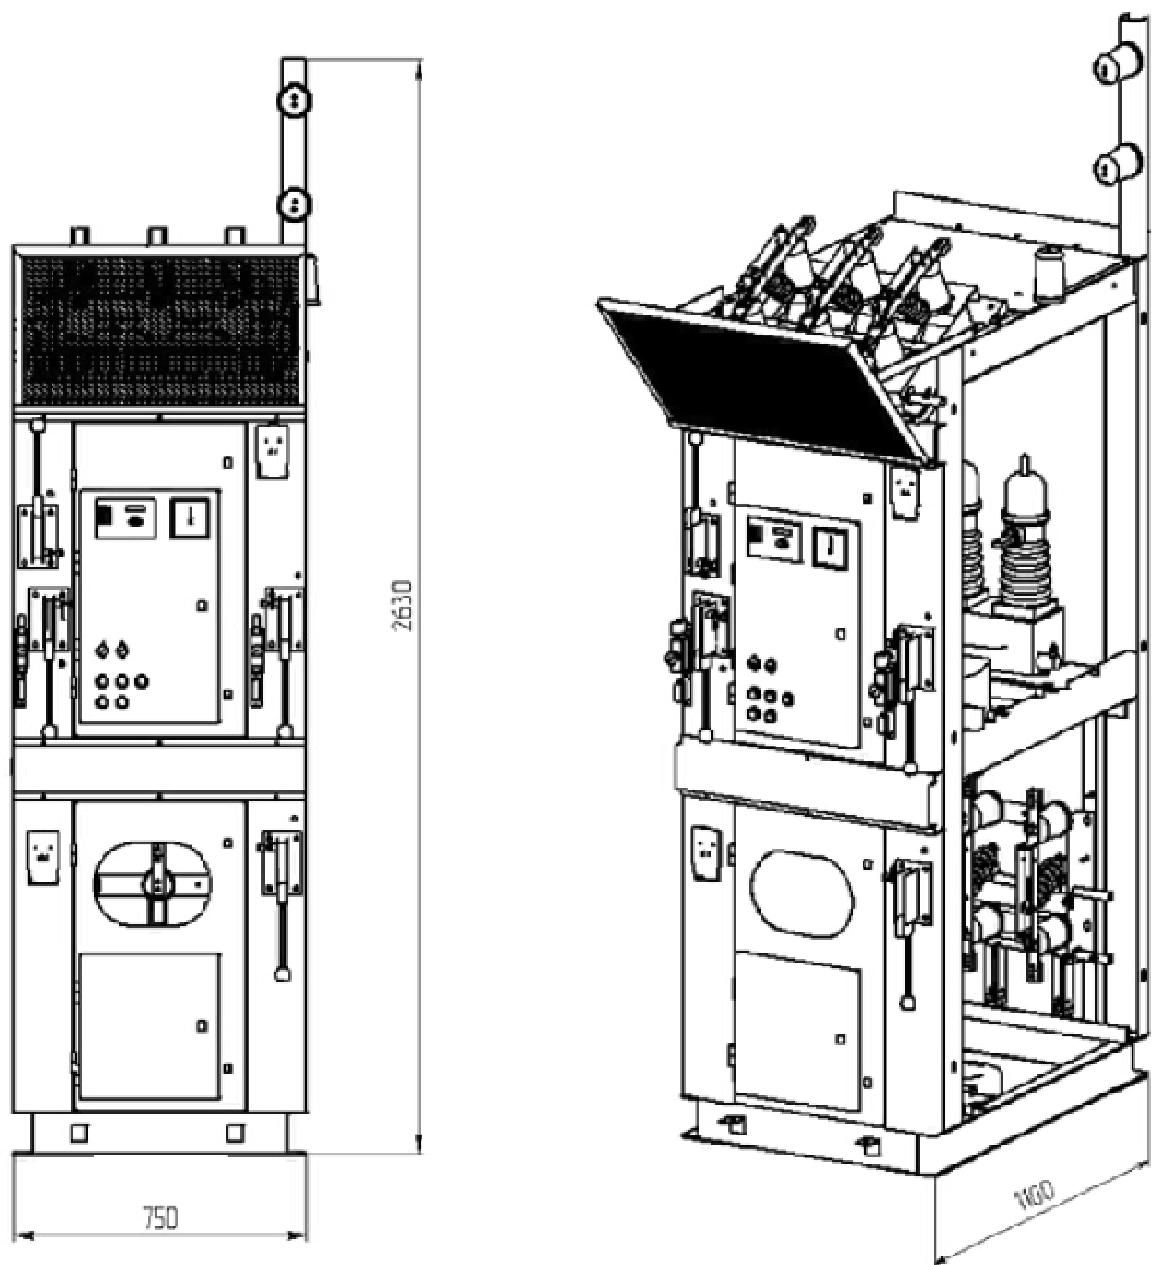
Габаритные размеры и общая компоновка камер КСО 298
